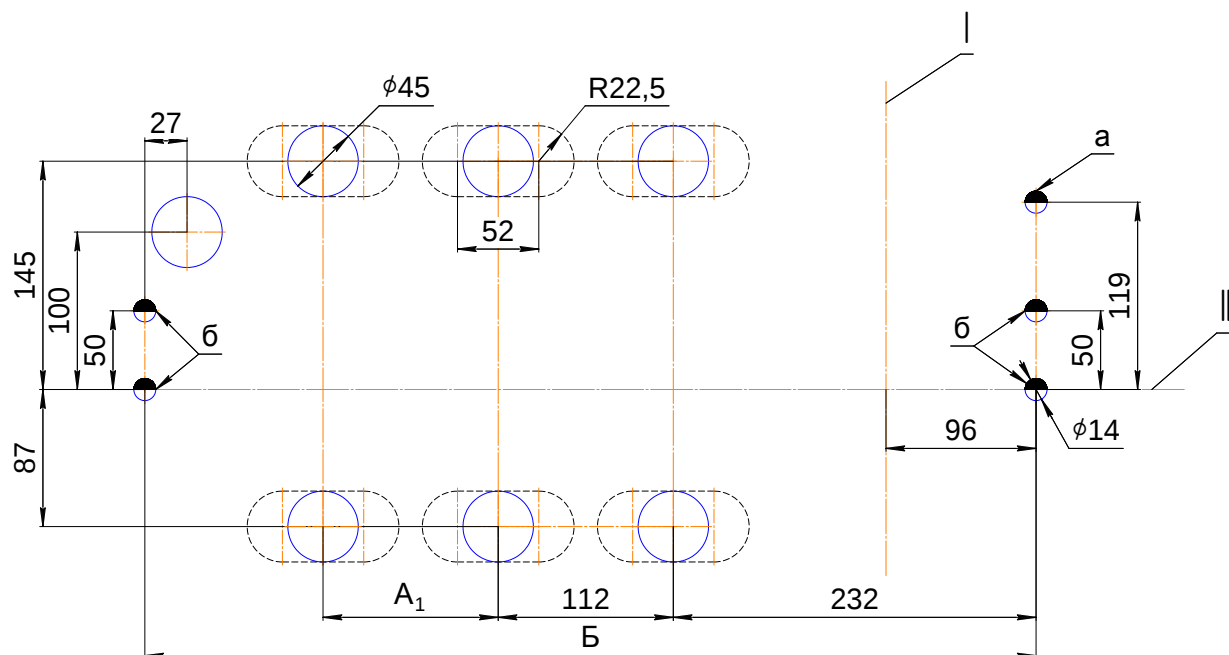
Расположение отверстий на плите для установки контакторов КТ6050/3
